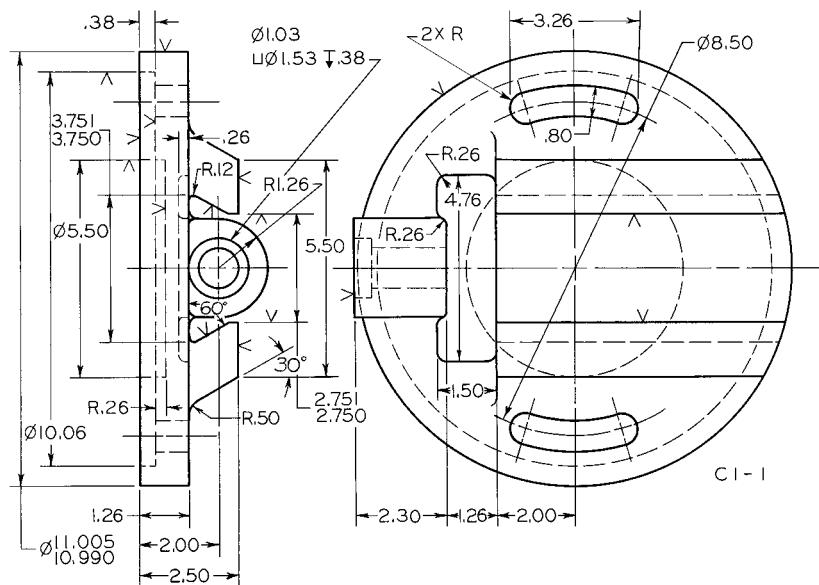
■ Disco ranurado para máquina de enrosque. Vistas dadas: Frontal e izquierdo. Vistas requeridas: frontal y derecha y superior en sección completa. Dibuje a la mitad del tamaño en el esquema B-4 o A3-4 (ajustado).
